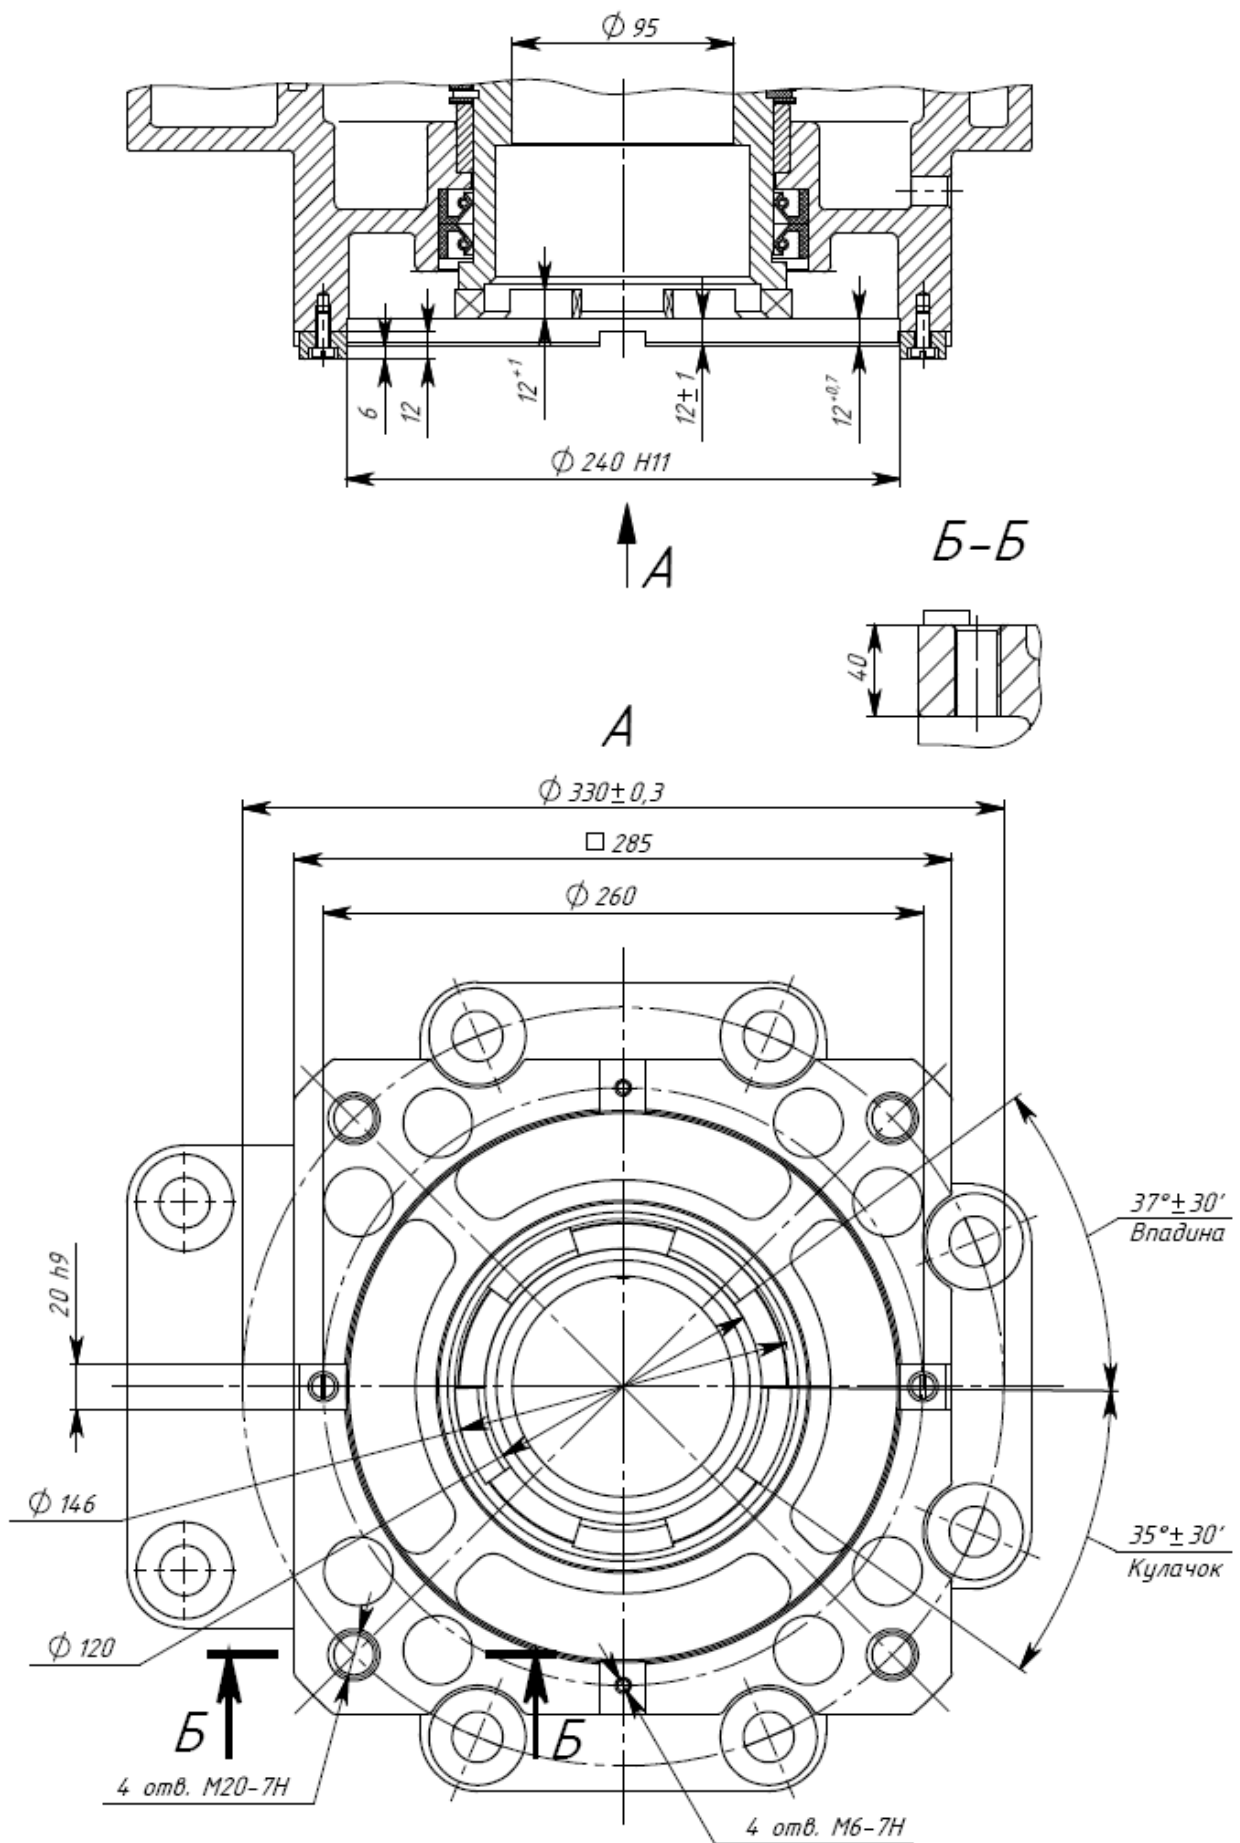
Присоединение типа Г для конструктивной схемы 43
